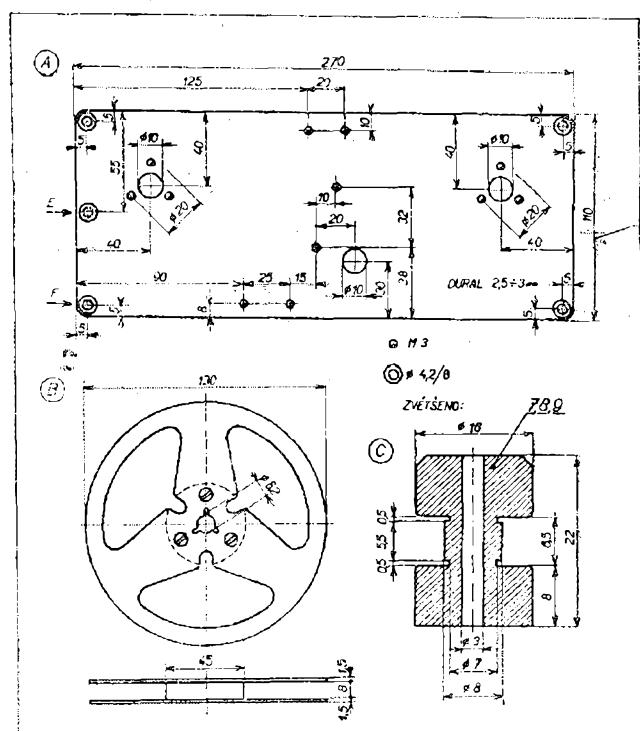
je detail navíjecí kladky, která je spojena s hlavní kladkou gumovým remínkem (průměr asi 3 mm), který koupíme v prodejnách s gumovým zbožím (těsnící kroužky). Cívka s páskem pouze leží na kotoučku a pohybuje se jen třením (na rozdíl od převíjecí kladky, kde je cívka unášena količkem). Pro zlepšení tření (a omezení hlu-
